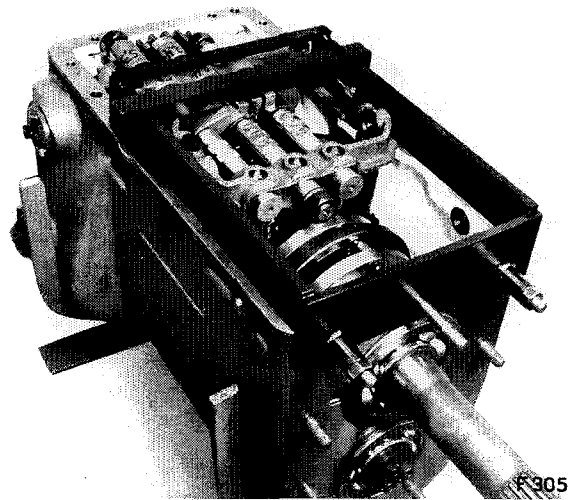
Aufgebaute Einstellehre mit Stahllineal
